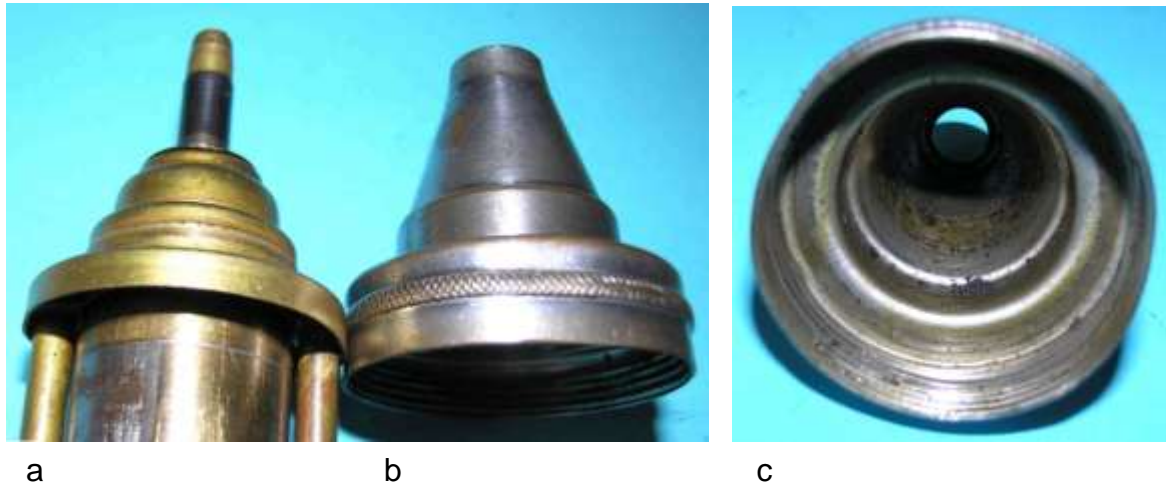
Anpassung des oberen Lagerschilds an den Lagerhals: a) Lagerschild mit Stehbolzen, b) und c) Lagerhals
